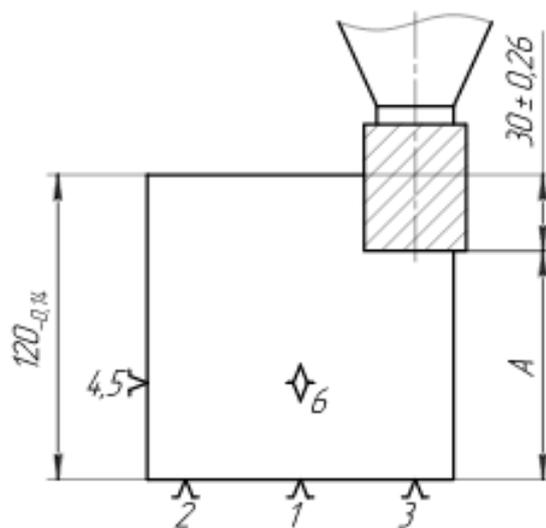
Схема механической обработки заготовки к задаче 3.10
